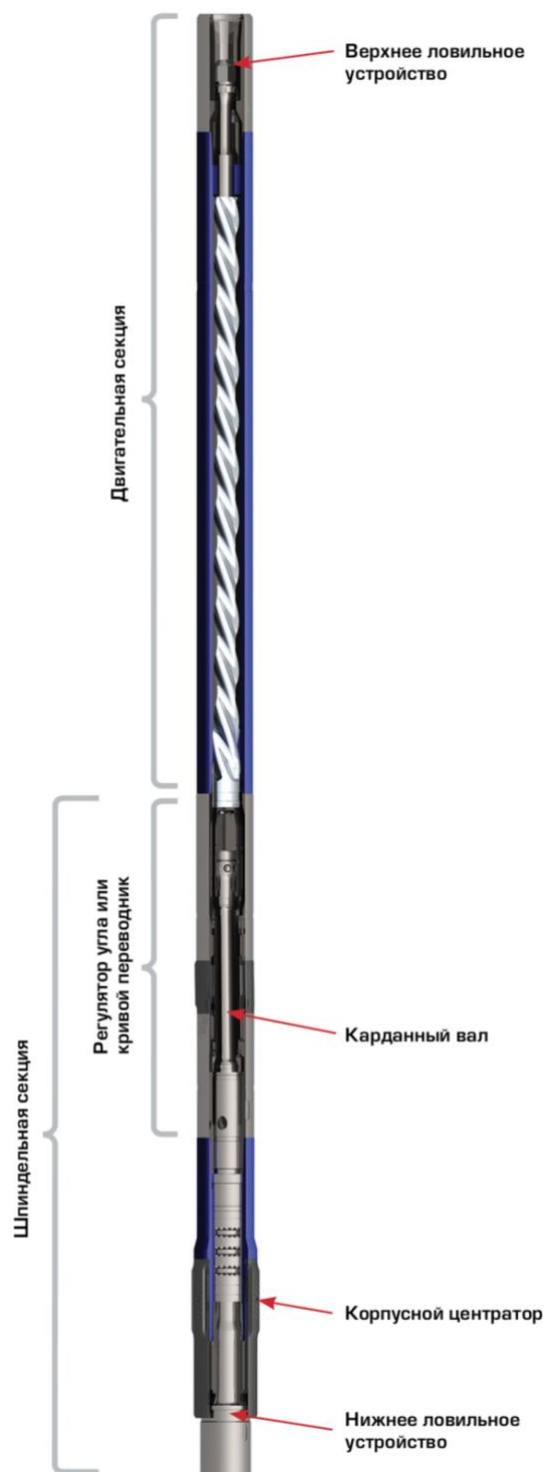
Основные узлы винтового забойного двигателя
